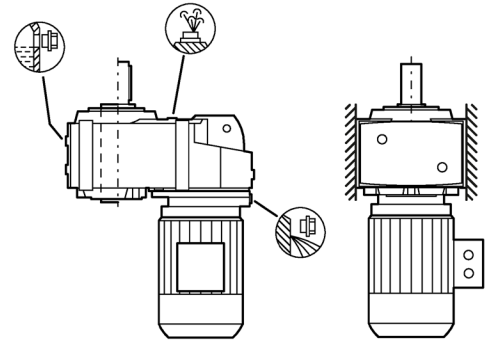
Einbaulagen für Flachgetriebe F. Fußausführung Baugröße 29
